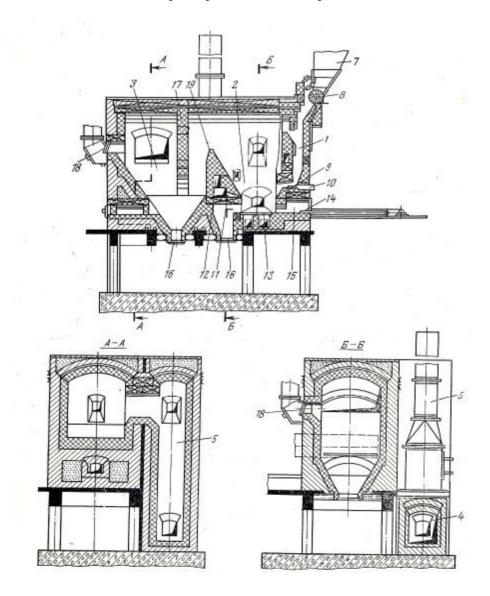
Факельно-слоевая топка системы проф. С.В.Татищева: 1- подсушивающая шахта; 2- камера сгорания; 3- камера дожигания; 4- боров; 5- вертикальный канал; 6- растопочная труба; 7- бункер; 8- питатель-дозатор; 9- распределительный стол; 10- сопла пневмозаброса; 11- сопла отсекающего дутья; 12- сопла вторичного дутья; 13- колосниковая решетка; 14- шурующая планка; 15- ниша; 16- затвор шлакового бункера; 17- разделительная стенка; 18- взрывной клапан; 19- задняя горка.
